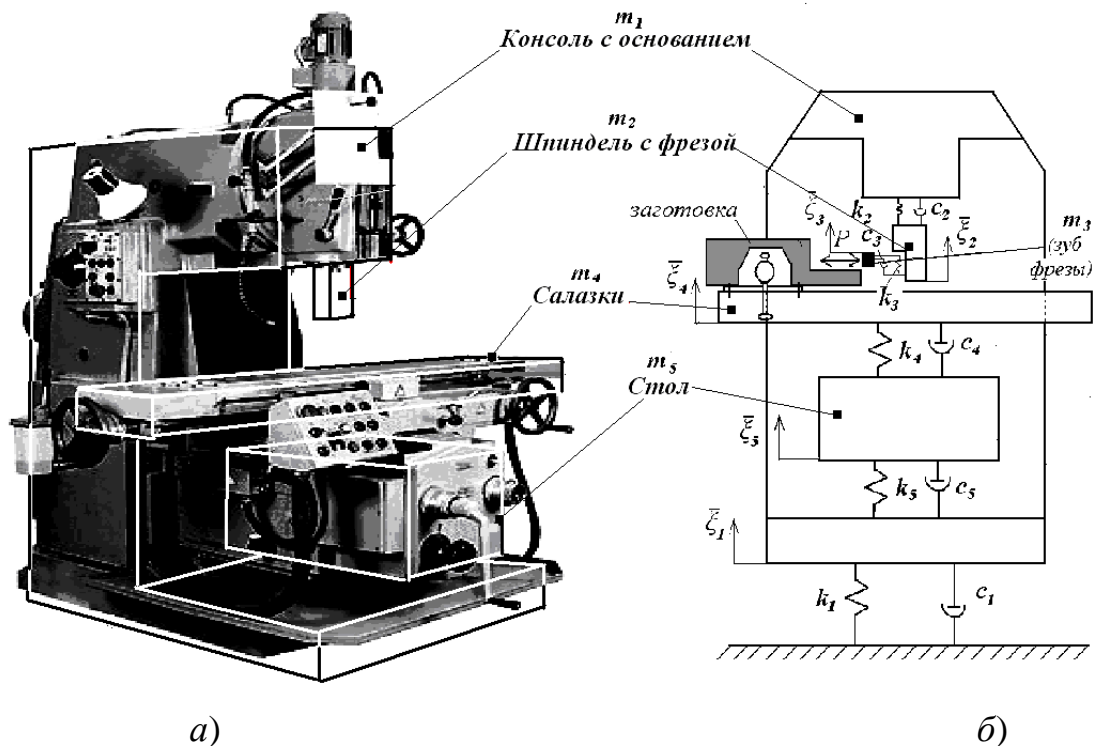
Моделируемые узлы обрабатывающей системы фрезерного станка *а)* и его динамическая модель *б)
